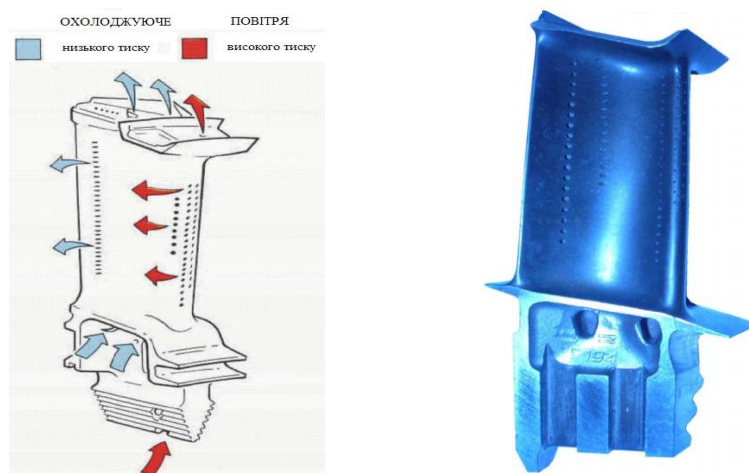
Робоча лопатка 1-го ступеню турбіни ТРДД Д-18Т
